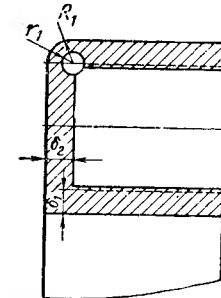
Конструктивная схема расчета цилиндрической части блока тормозных цилиндров
